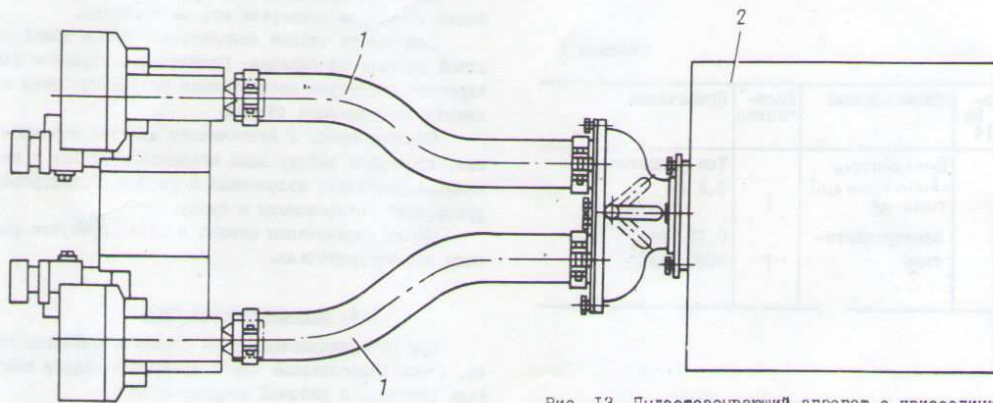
Пылетсасывающий агрегат с соединительными деталями
